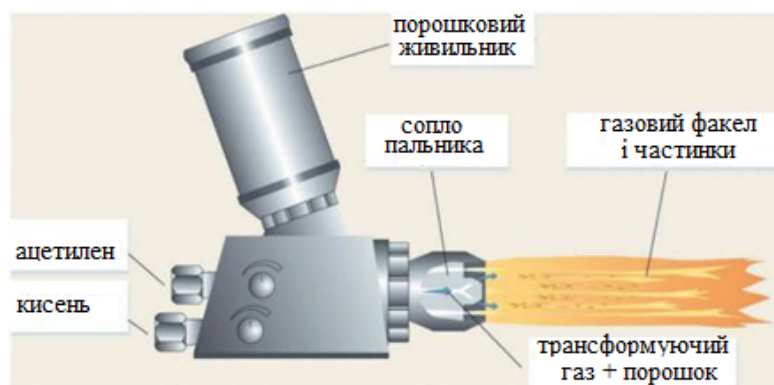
Схема пальника для газополум'яного порошкового напилення
